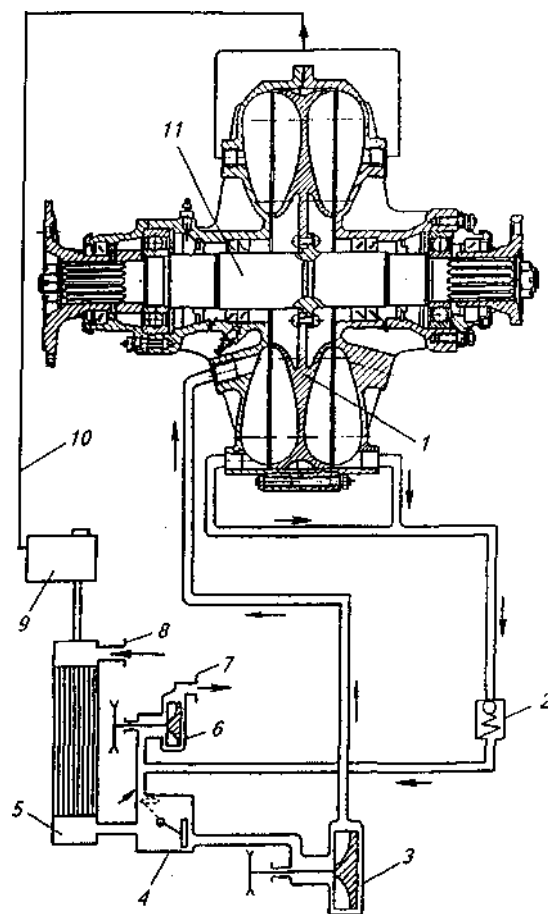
Двухлопастный гидрозамедлитель: 1 — ротор; 2 — подпорный клапан; 3 — насос; 4 — клапан; 5 — радиатор; 6 — помпа; 7, 8 — каналы; 9 — компенсационный бачок; 10 — дренажный канал; 11 — вал
